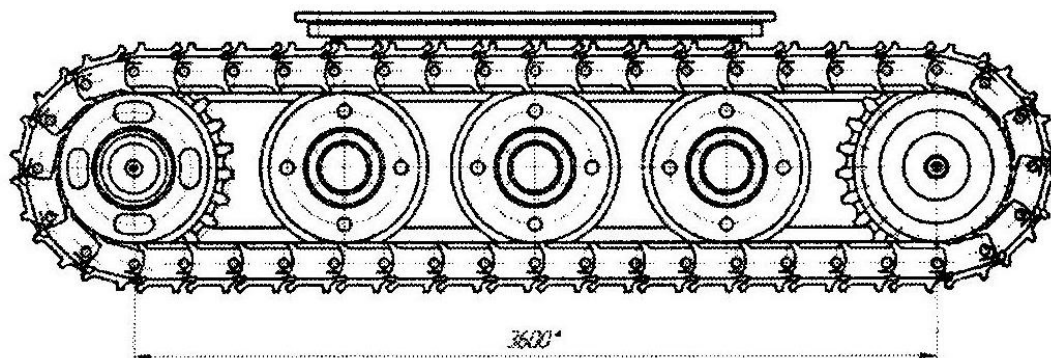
Общий вид экскаваторного гусеничного движителя.
